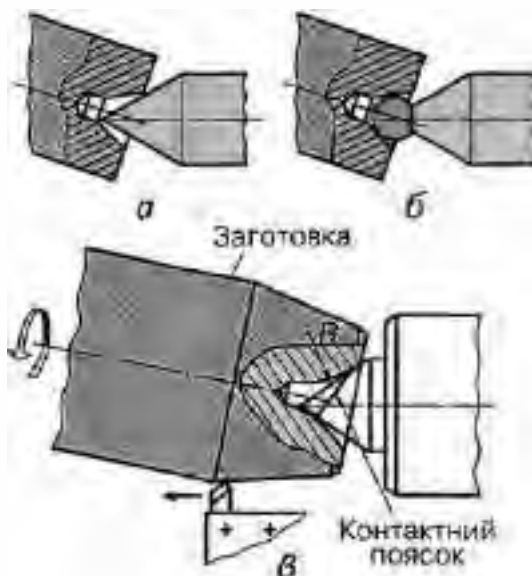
ПОЛОЖЕННЯ ЗАГОТОВКИ НА ЗМІЩЕНИХ ЦЕНТРАХ:
